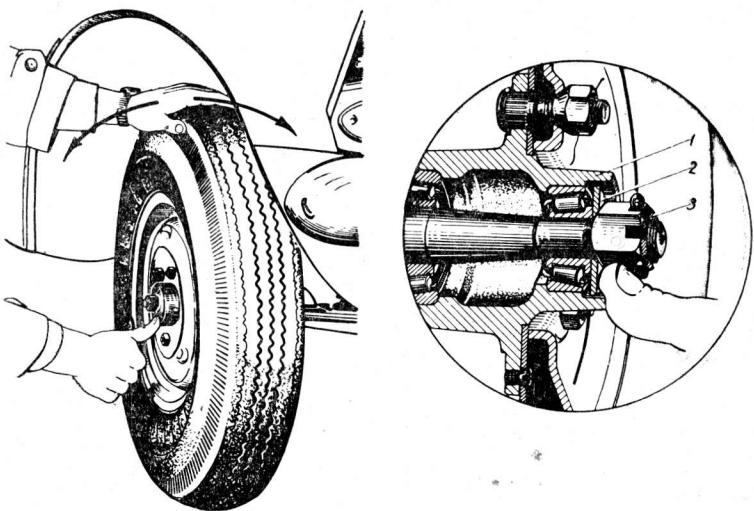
Проверка подтяжки подшипников ступицы переднего колеса:
